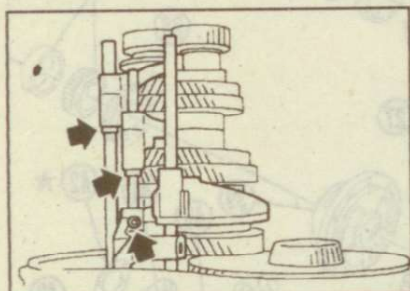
Расположение стопорных колец и штифтов крепления вилок 5-й, 3-й и 4-й передач
